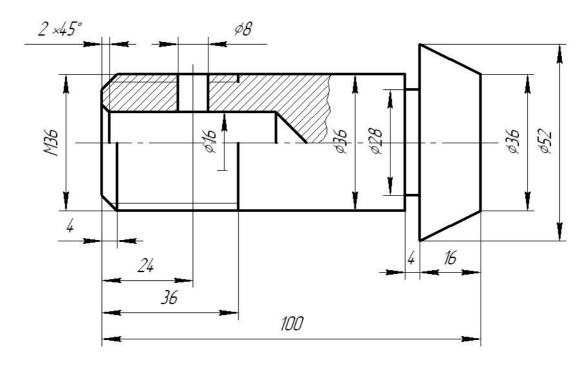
Чертеж детали с осевыми размерами (допуски на все конструкторские размеры должны быть известны)
